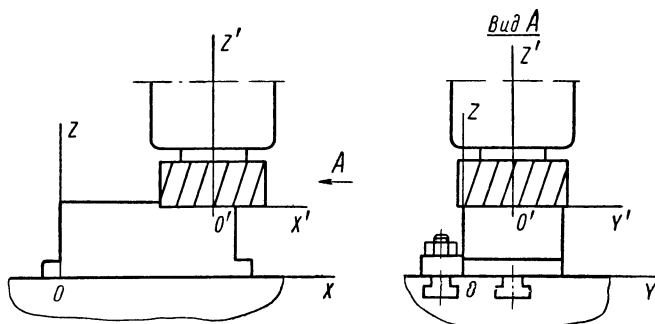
Совмещение систем координат с режущим инструментом и базами станка на вертикально-фрезерном станке
